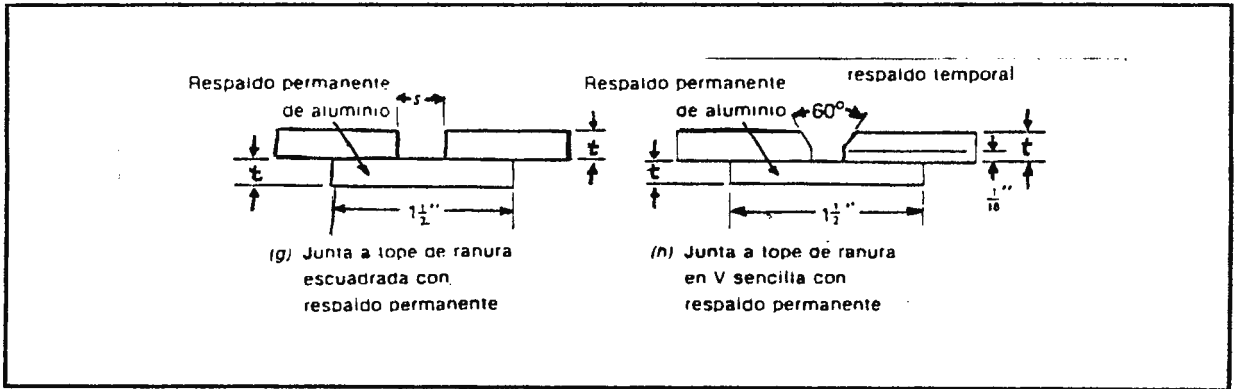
Junta de uso común en la soldadura de aluminio
